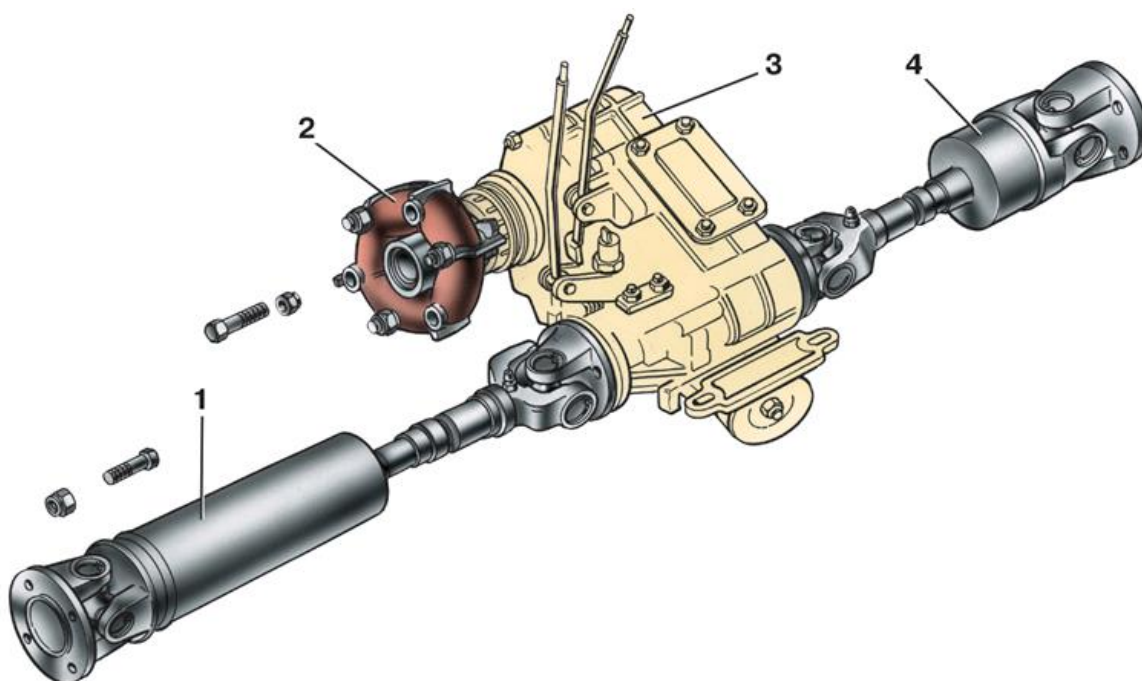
Карданная передача автомобиля ВАЗ-21213: 1 - передний карданный вал; 2 - промежуточный карданный вал; 3 - раздаточная коробка; 4 - задний карданный вал
